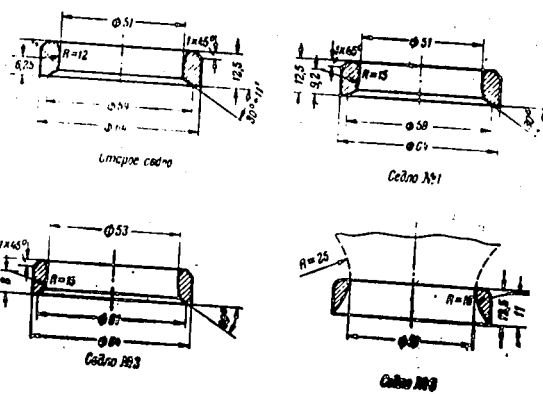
Vier Formen der untersuchten Einlaßventil-Sitzringe (Koroljev)
